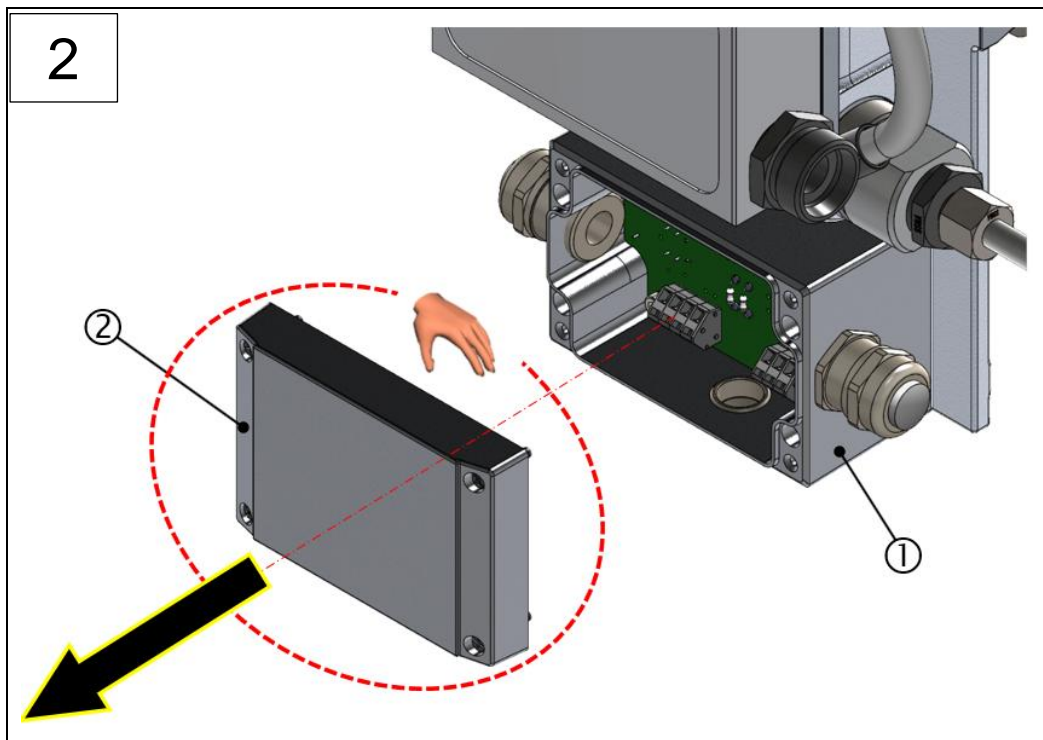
Caja de bornes de VN2020: desmontaje del tapa (pasos de montaje 1-2)
